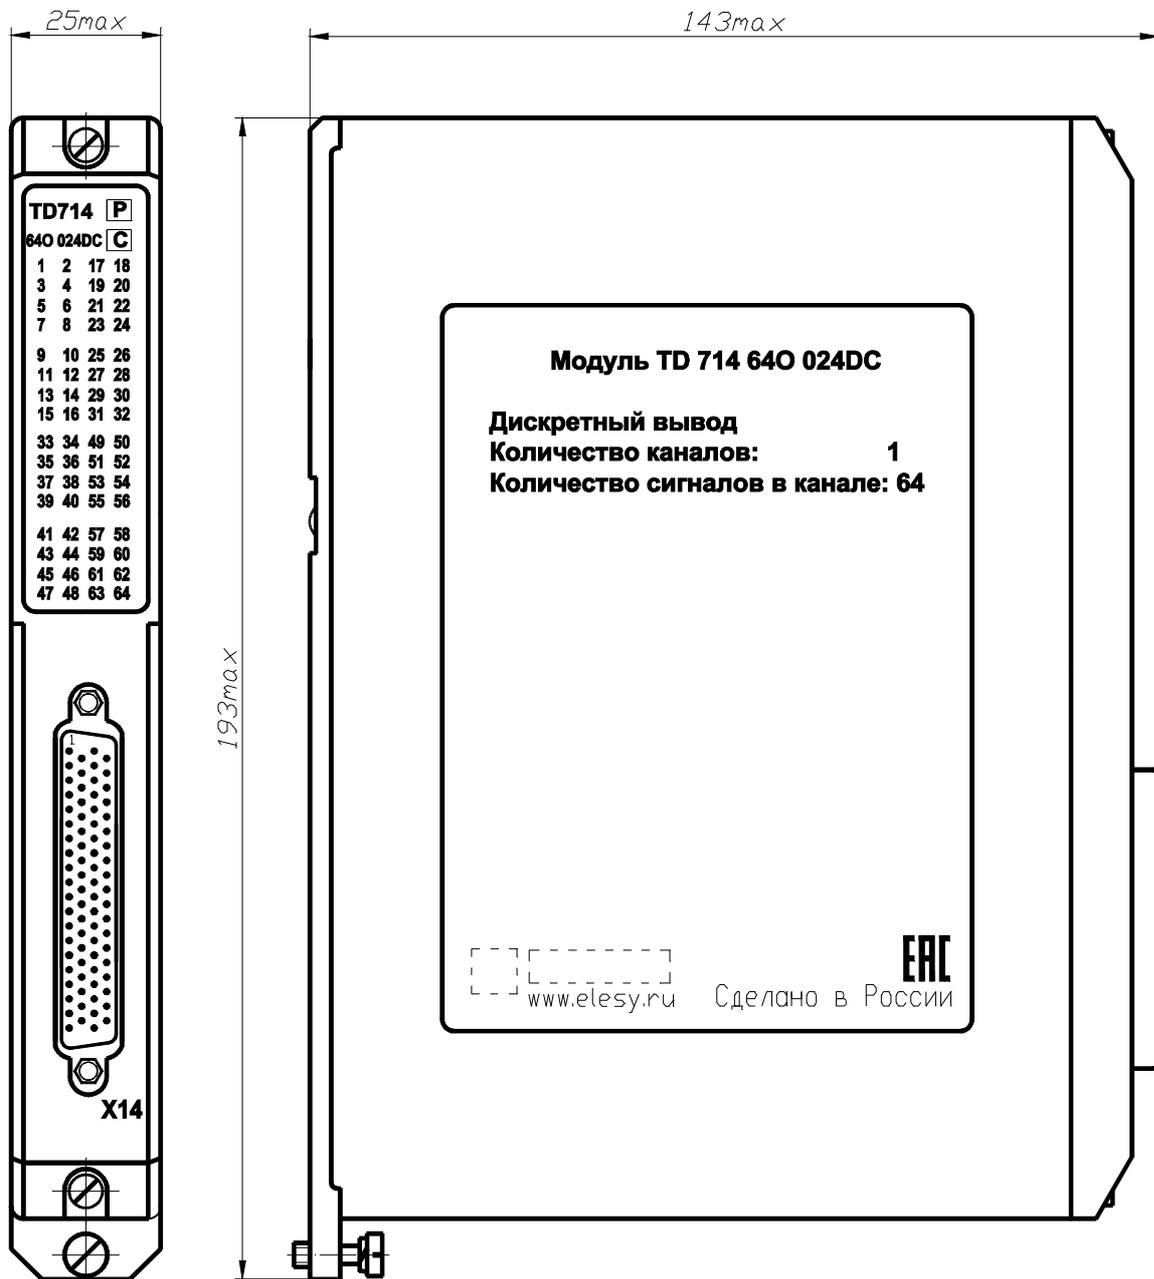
Внешний вид и габаритные размеры модуля
